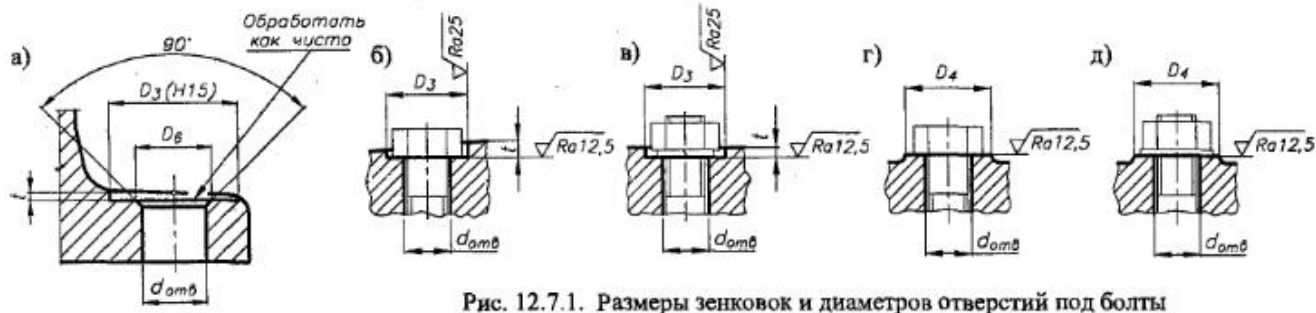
Размеры зенковок и диаметров отверстий под болты
